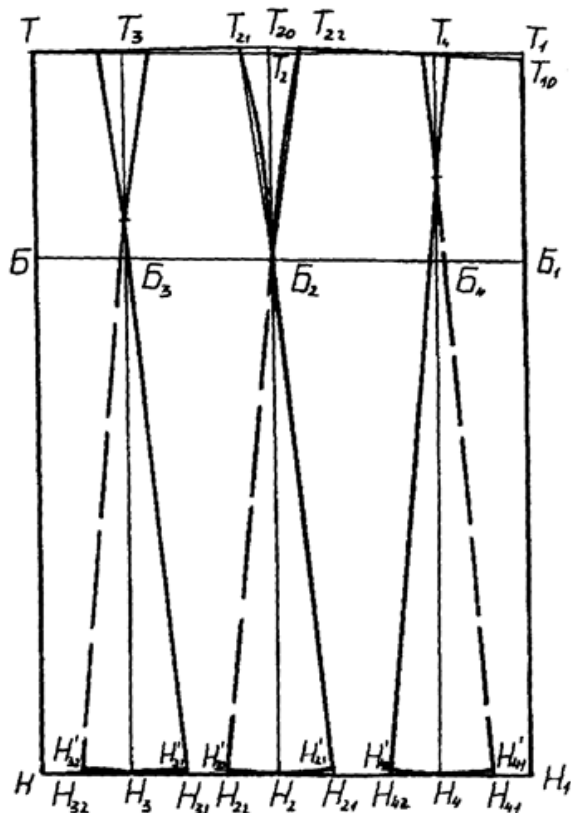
Чертеж конструкции шестиклиньевой юбки с прямолинейным расширением к низу
